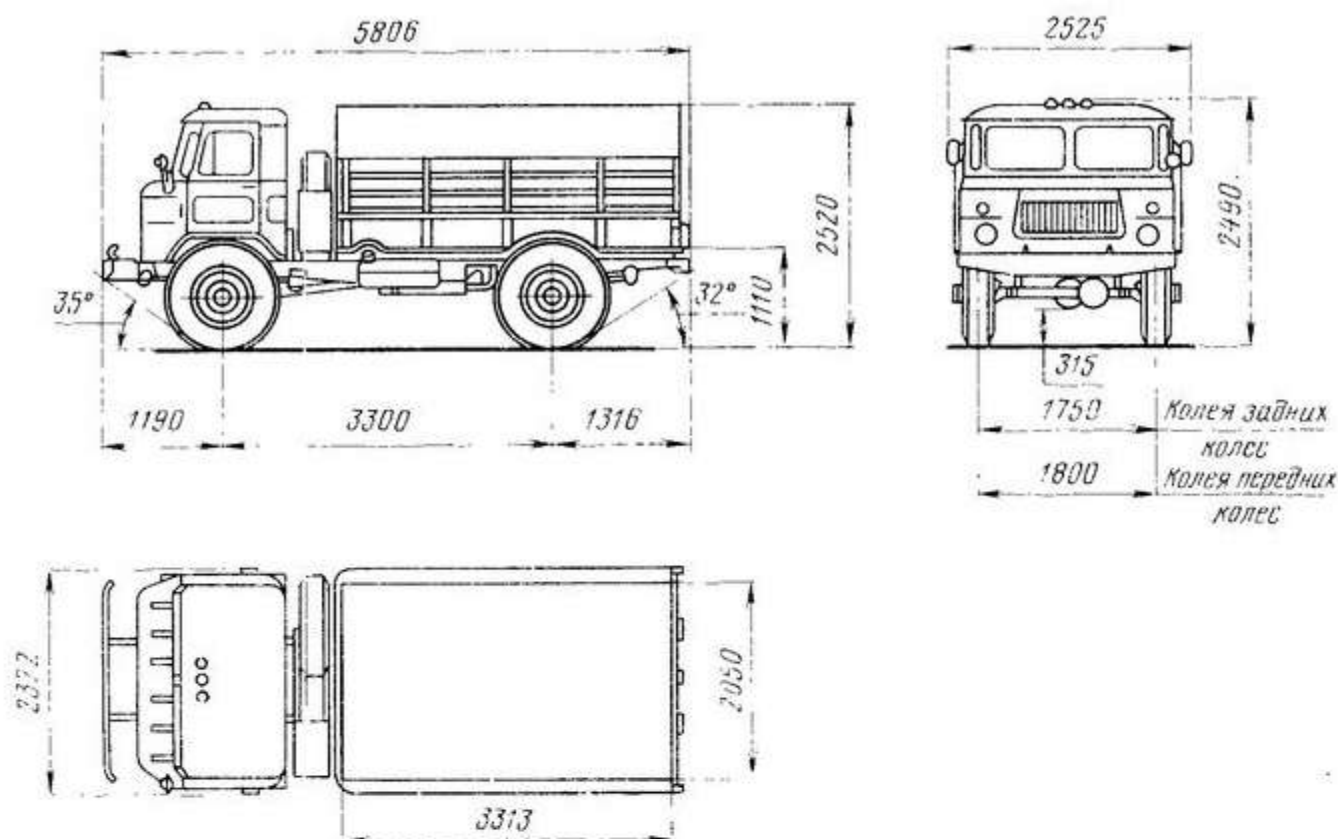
Габаритные размеры автомобиля ГАЗ-66-11
